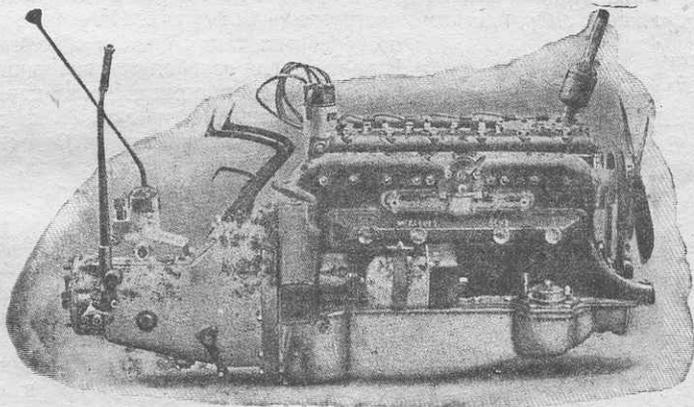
Группа двигателя, сцепления и коробки передач 2-литровой модели «Мерседес-Бенц».
